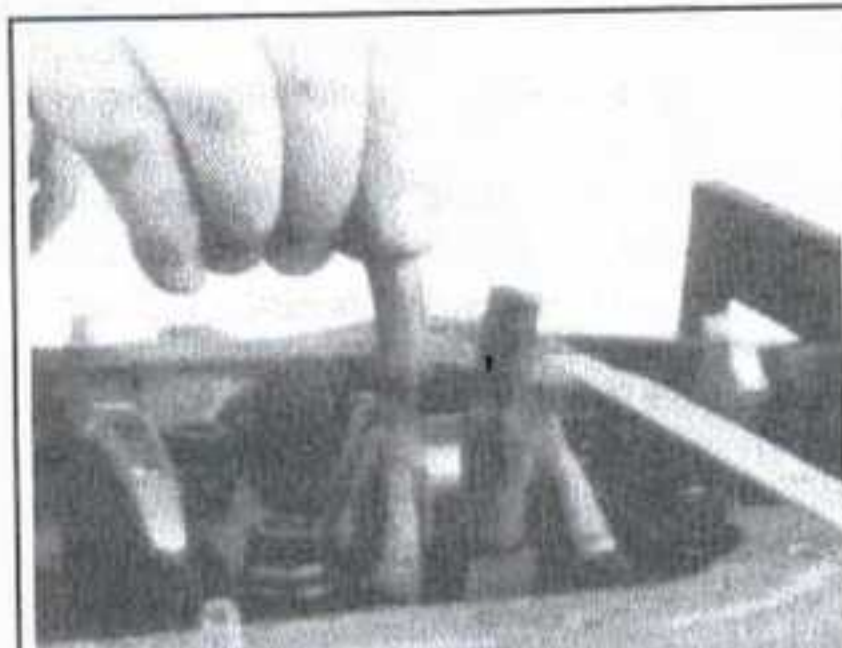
Наденьте отрезок резинового шланга на шпильки шатуна, чтобы не повредить коленчатый вал и стенки цилиндров
